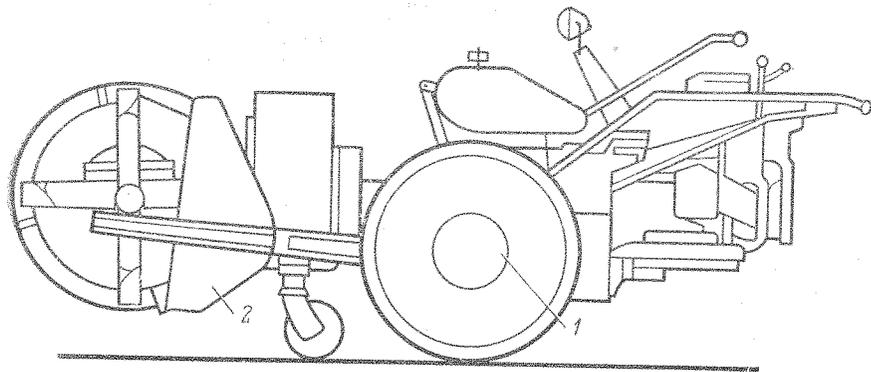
Общий вид малогабаритного фрезерно-роторного снегоочистителя МС-59:
